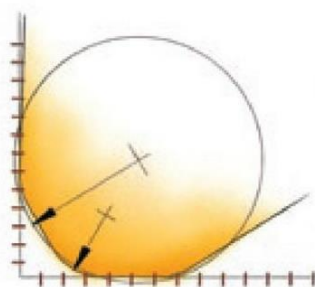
Схема вершины режущей части инструмента по технологии Wiper
